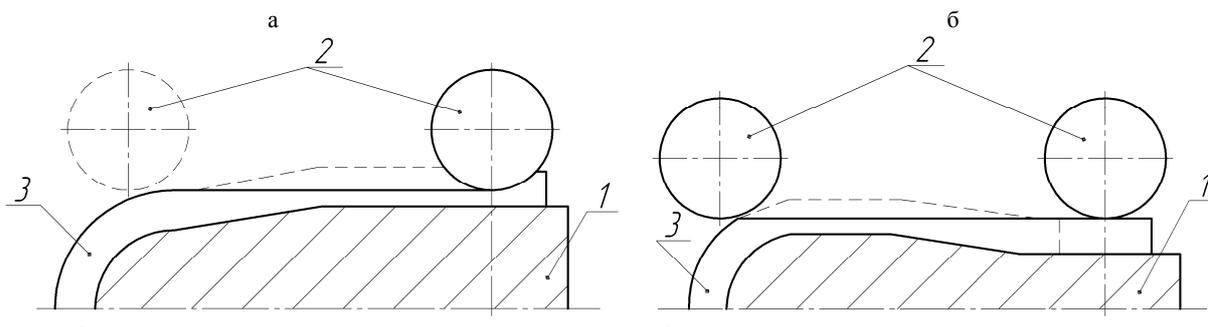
Схемы прокатки: а) - с нарастающим обжатием, б) - с убывающим обжатием: 1 – профильная оправка; 2 – прокатные валки; 3 – заготовка
